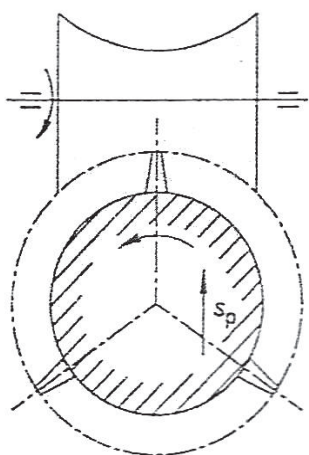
Схема нарезания глобоидного червяка на зубофрезерном станке специальной резцовой головкой
